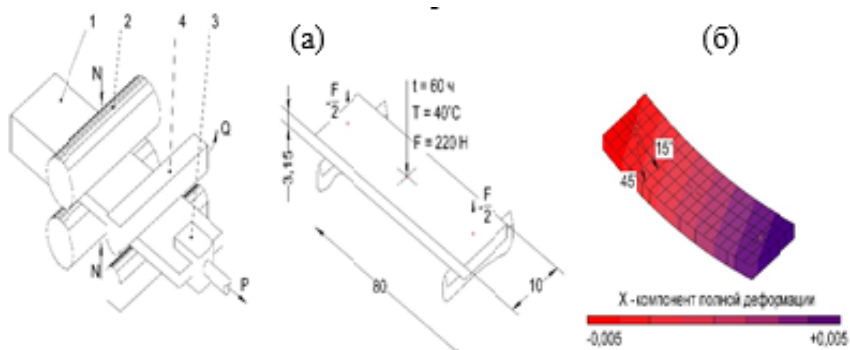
Схема (а) получения пластины Al–Mg–SiC (образца) в валах-кристаллизаторах: 1 – ж-т расплав, 2 – валок-кристаллизатор; 3- механизм прокатки; 4 – формирование заготовки; и (б) пример испытания образца на изгиб (Эфиопия)
